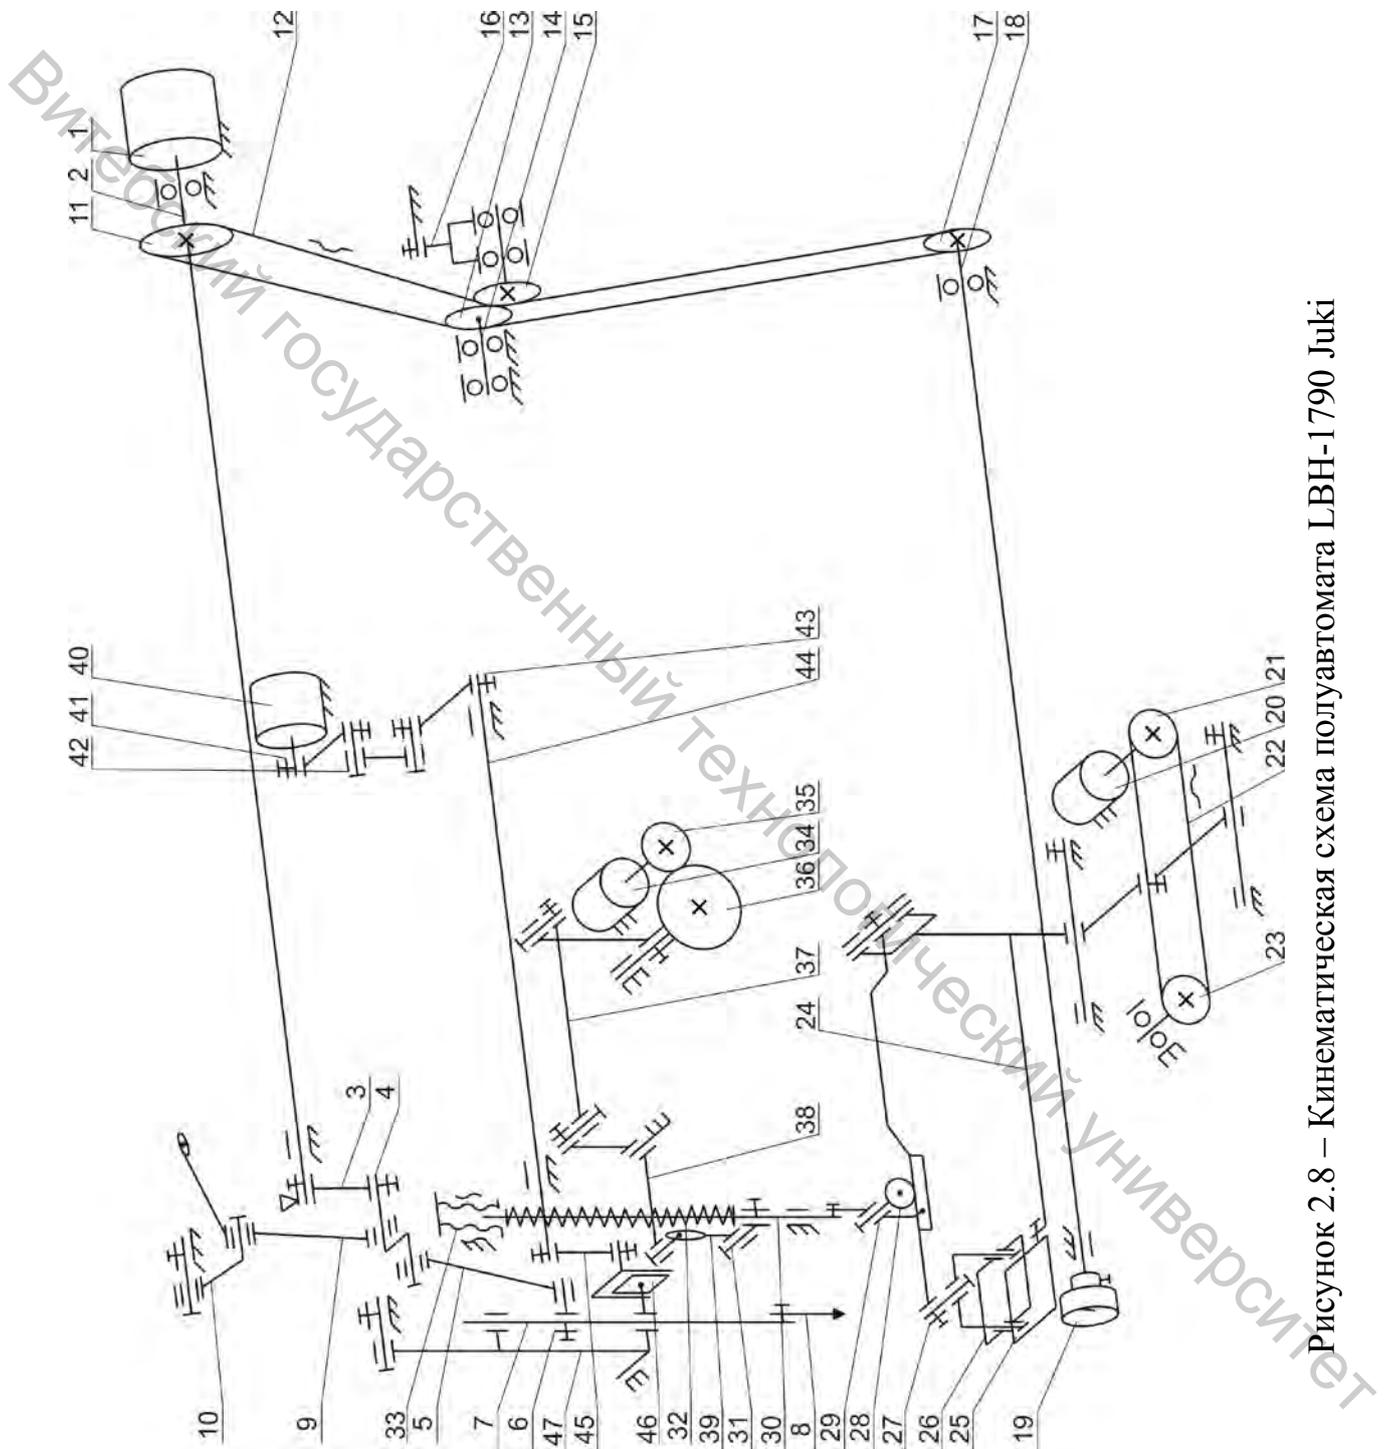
Кинематическая схема полуавтомата LBN-1790 Juki
